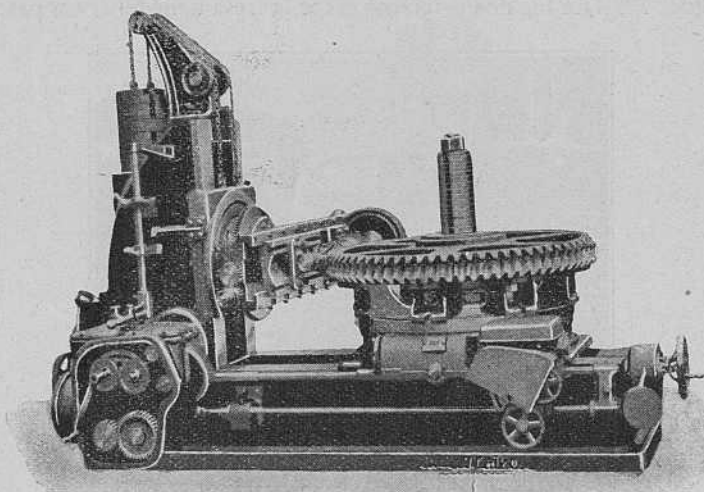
Máquina Renania cortando engranajes de visinfín.
